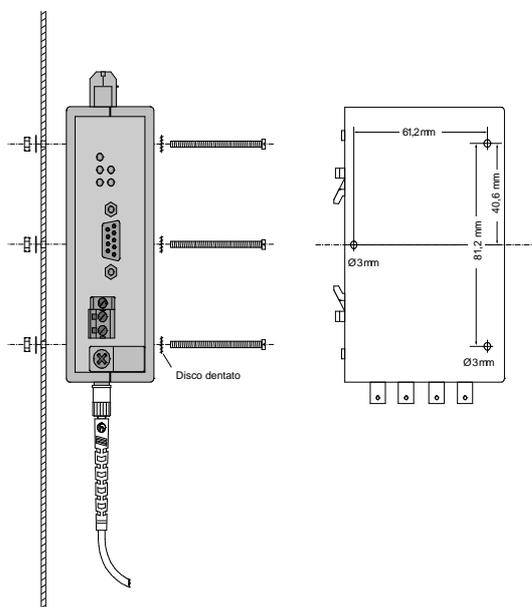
Montaggio di un modulo su una piastra di montaggio
